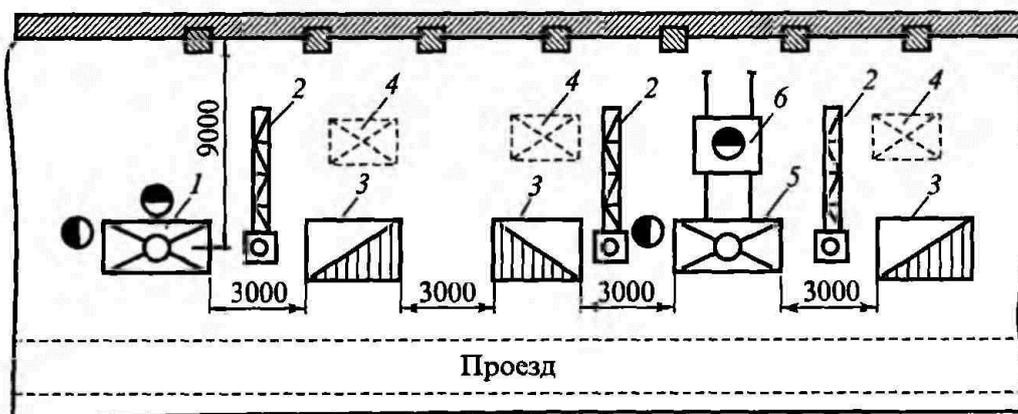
Планировка участкаковки и штамповки деталей в кузнечном цехе: 1 — ковочный молот, обслуживаемый одной нагревательной печью; 2 — поворотный край; 3 — печи; 4 — площадки для заготовок; 5 — ковочный молот, обслуживаемый двумя нагревательными печами; 6 — ковочный манипулятор
